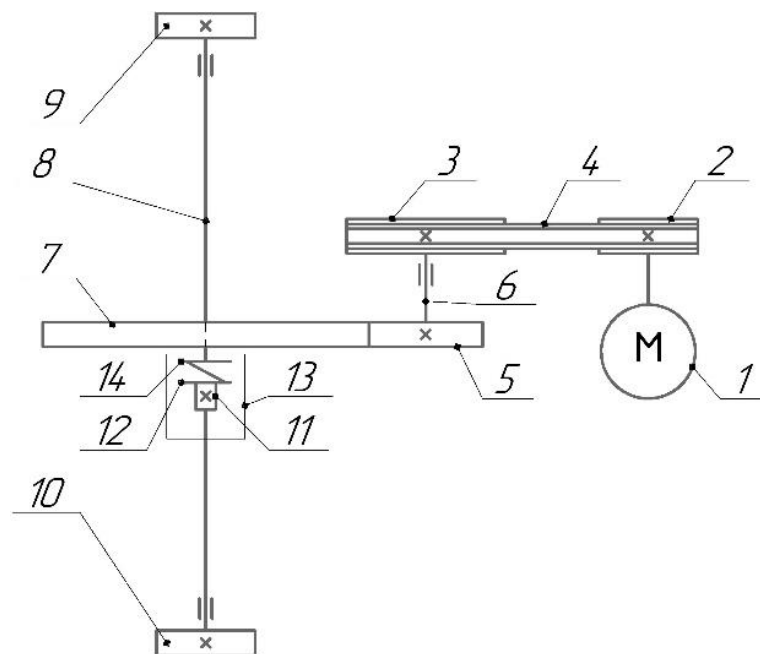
Кінематична схема привода круглов'язальної машини: 1 - електродвигун; 2 та 3- ведучий та ведений шківів клинопасової передачі; 4 - паси; 5 - ведуча шестерня; 6 - проміжний вал; 7 - зубчасте колесо; 8 - приводний вал; 9, 10 - шестерні; 11 - пружна запобіжна муфта; 12, 14 - півмуфти
